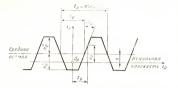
Параметры профиля инструментальной рейки для эвольвентных зубчатых колес
